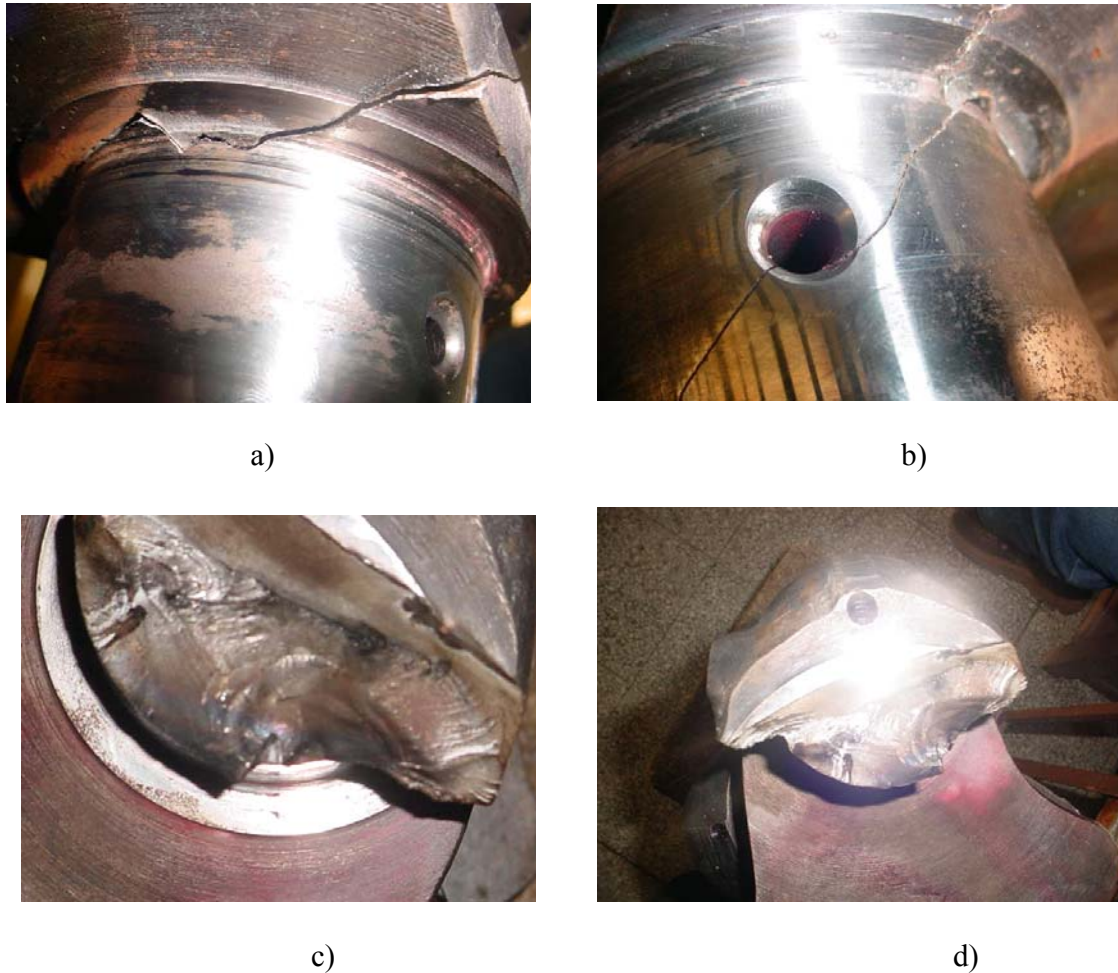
Vistas de la grieta de la fractura y del aspecto externo de la zona fracturada
